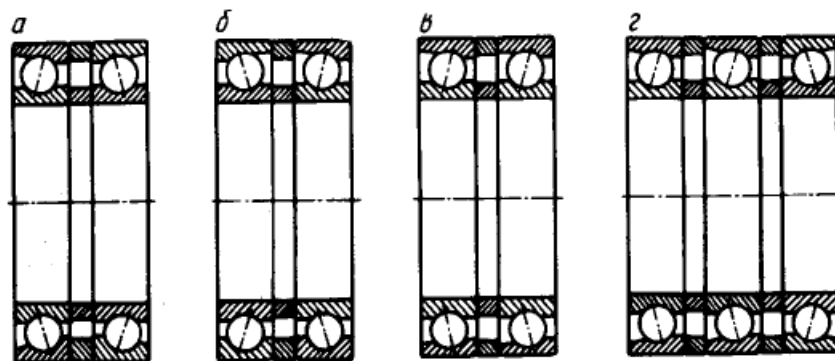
Компонування опор шпинделя з радіально-упорних підшипників
